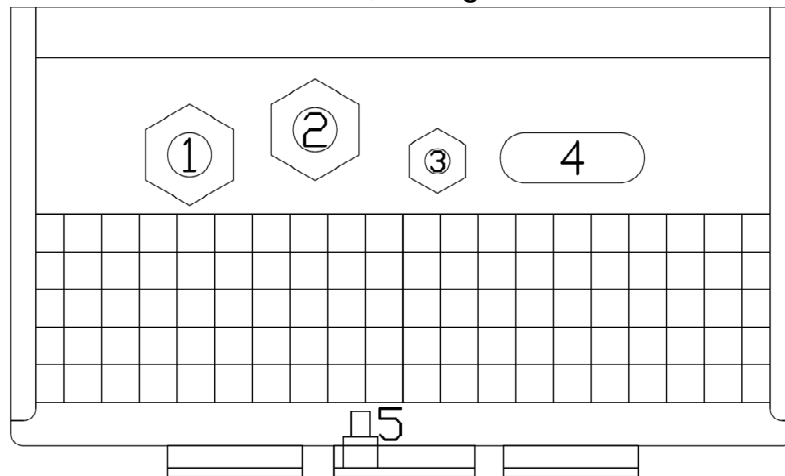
Gehäuse von unten mit Sicht auf die Kabeleinführungen
